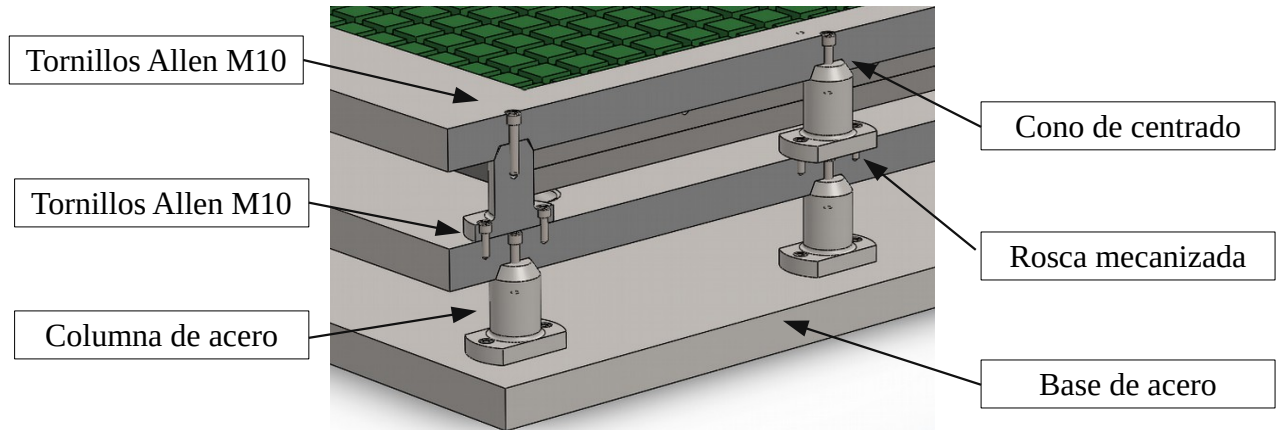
Sección transversal de la bancada con los anclajes a la vista.
